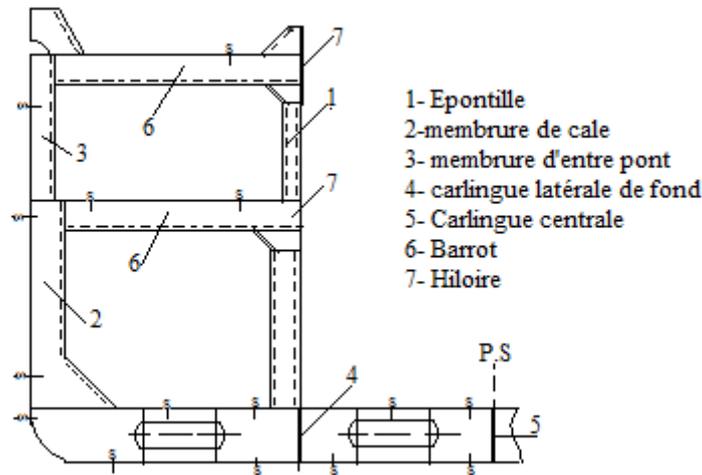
Section maitresse d'un cargo dans le système de raidissage transversal.
